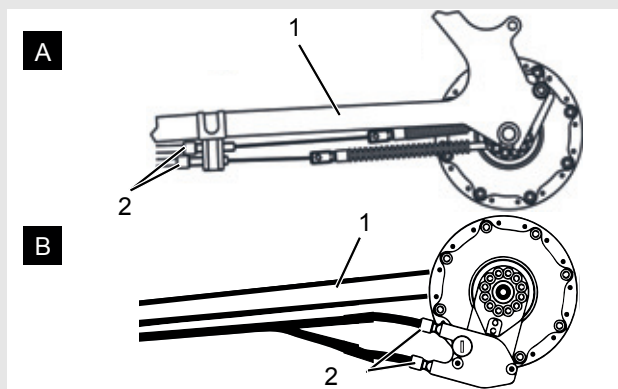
Seřizovací pouzdro (1) řazení převodů ovládané jedním lankem s řadicí páčkou (2) - příklad
